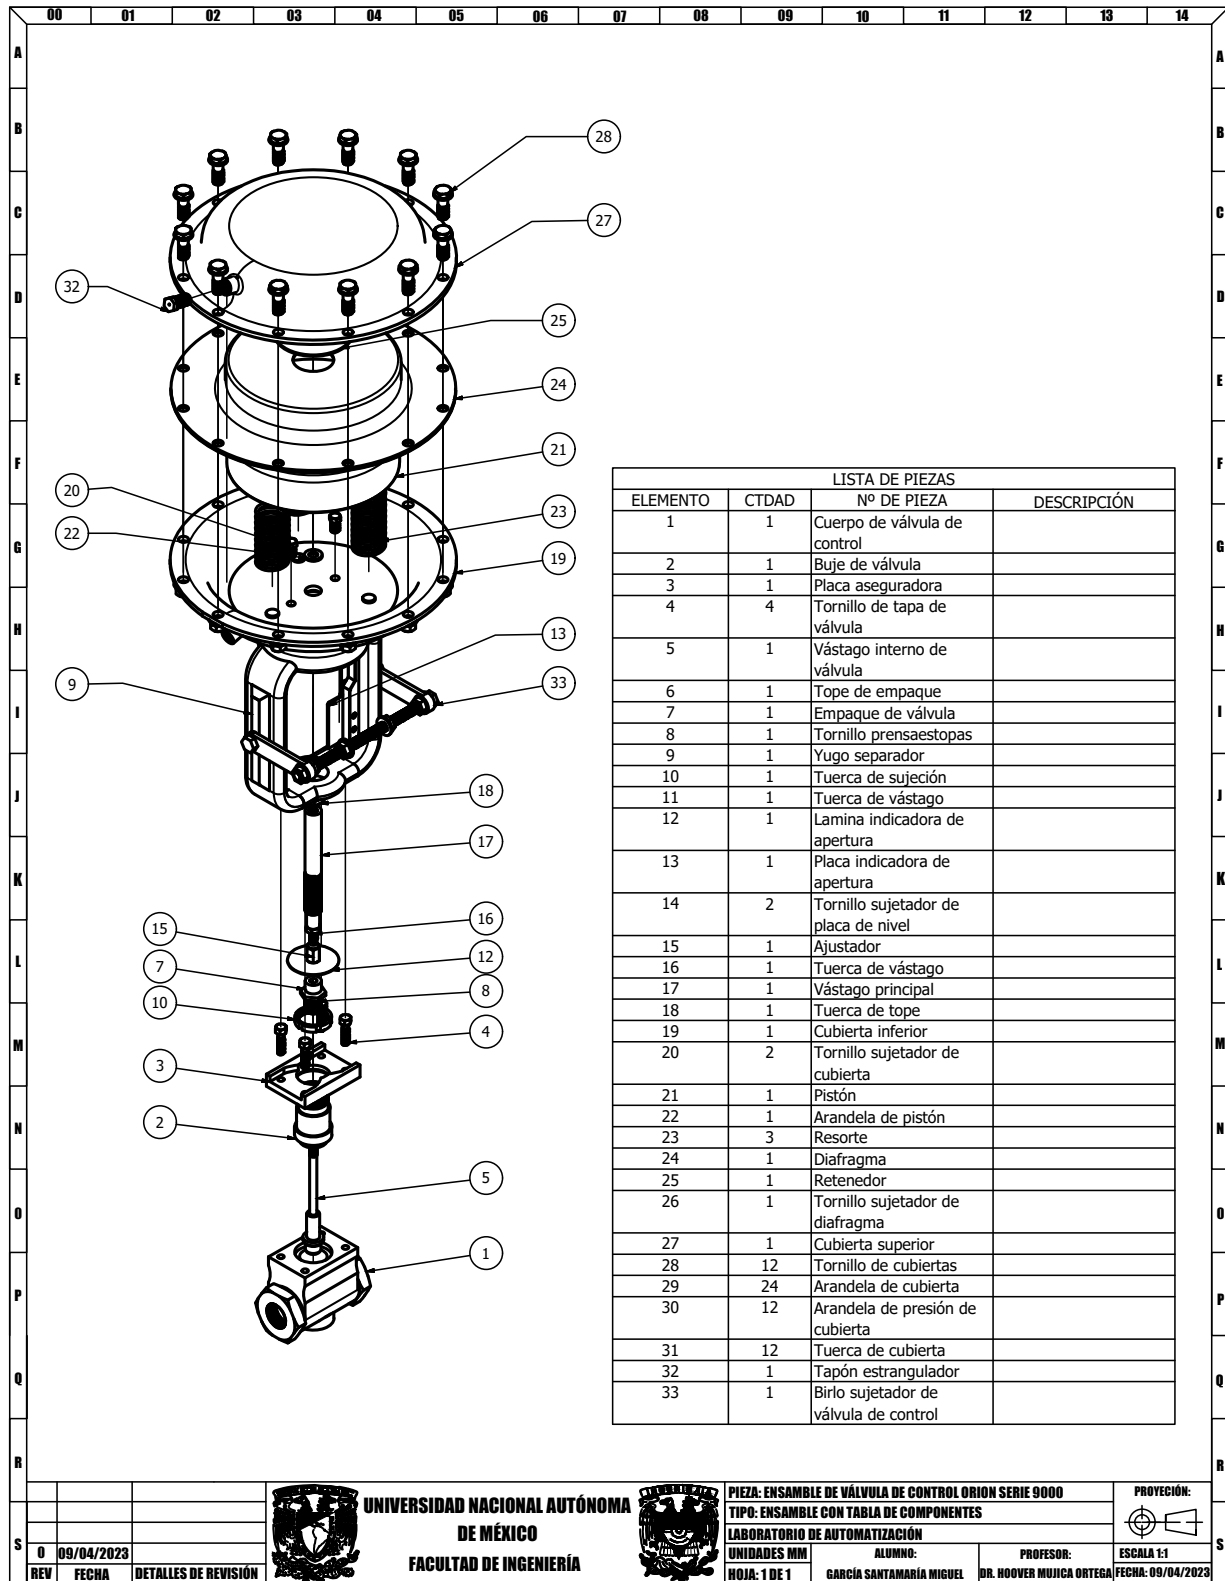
Ensamble explosionado y tabla de componentes de válvula de control Orion serie 9000
